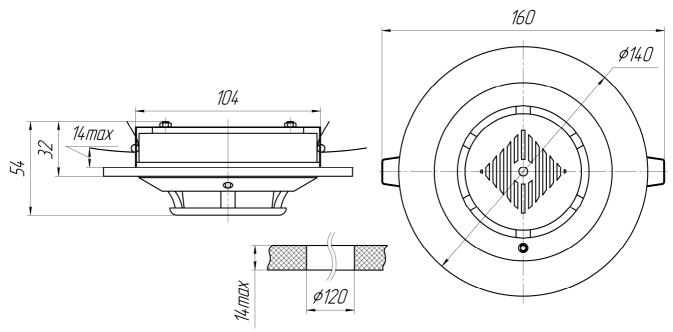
Внешний вид, габаритные и установочные размеры извещателей СПДОТА, СПДОТА-В при креплении через декоративное кольцо в подвесном потолке (исполнение IP30), размеры в мм.
